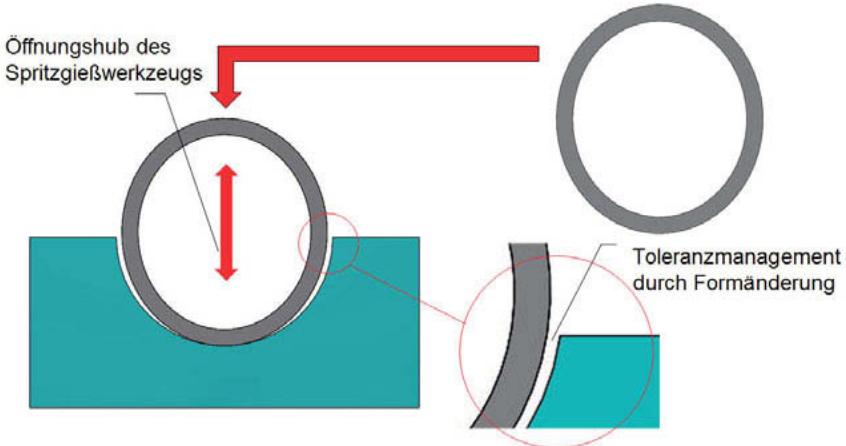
Gezielte Formänderung für reproduzierbares und prozesssicheres Abdichten zwischen Einleger und Spritzgießwerkzeug
